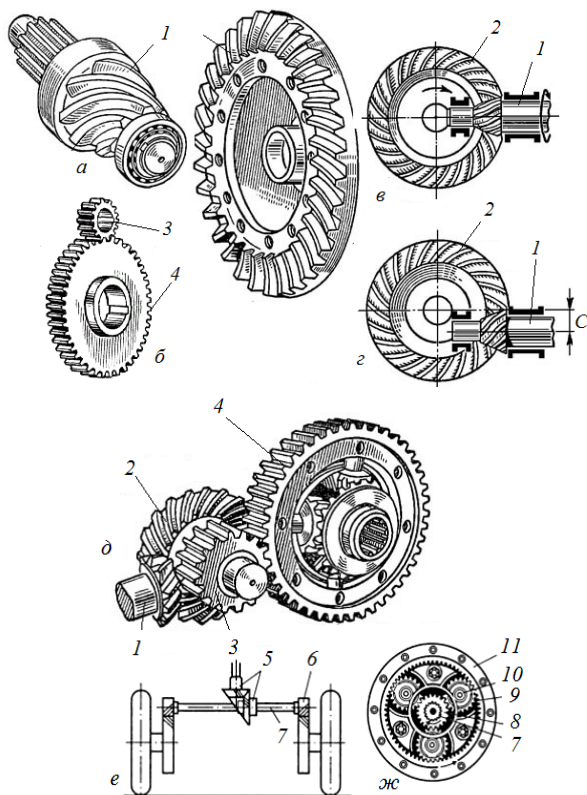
Схемы главных передач: а – устройство; б – цилиндрическая; в – коническая; г – гипоидная; д – двойная; е – разнесенная; ж – однорядный планетарный колесный редуктор: 1 – ведущая коническая шестерня; 2 – ведомое колесо; 3, 4 – цилиндрические шестерни; 5 – спиральные конические шестерни; 6 – цилиндрические шестерни; 7 – полуось; 8 – солнечная шестерня; 9 – сателлит; 10 – ось; 11 – коронная шестерня
